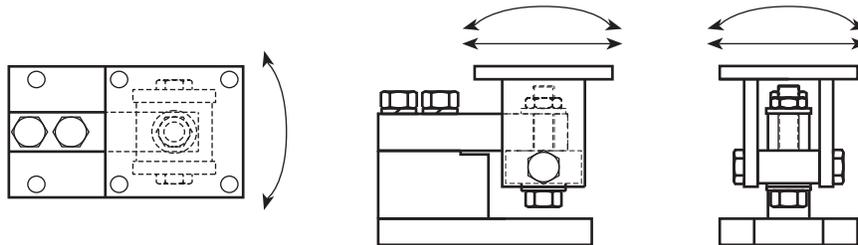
Módulos HE RL1800 y RL1855 en tanque cilíndrico horizontal
